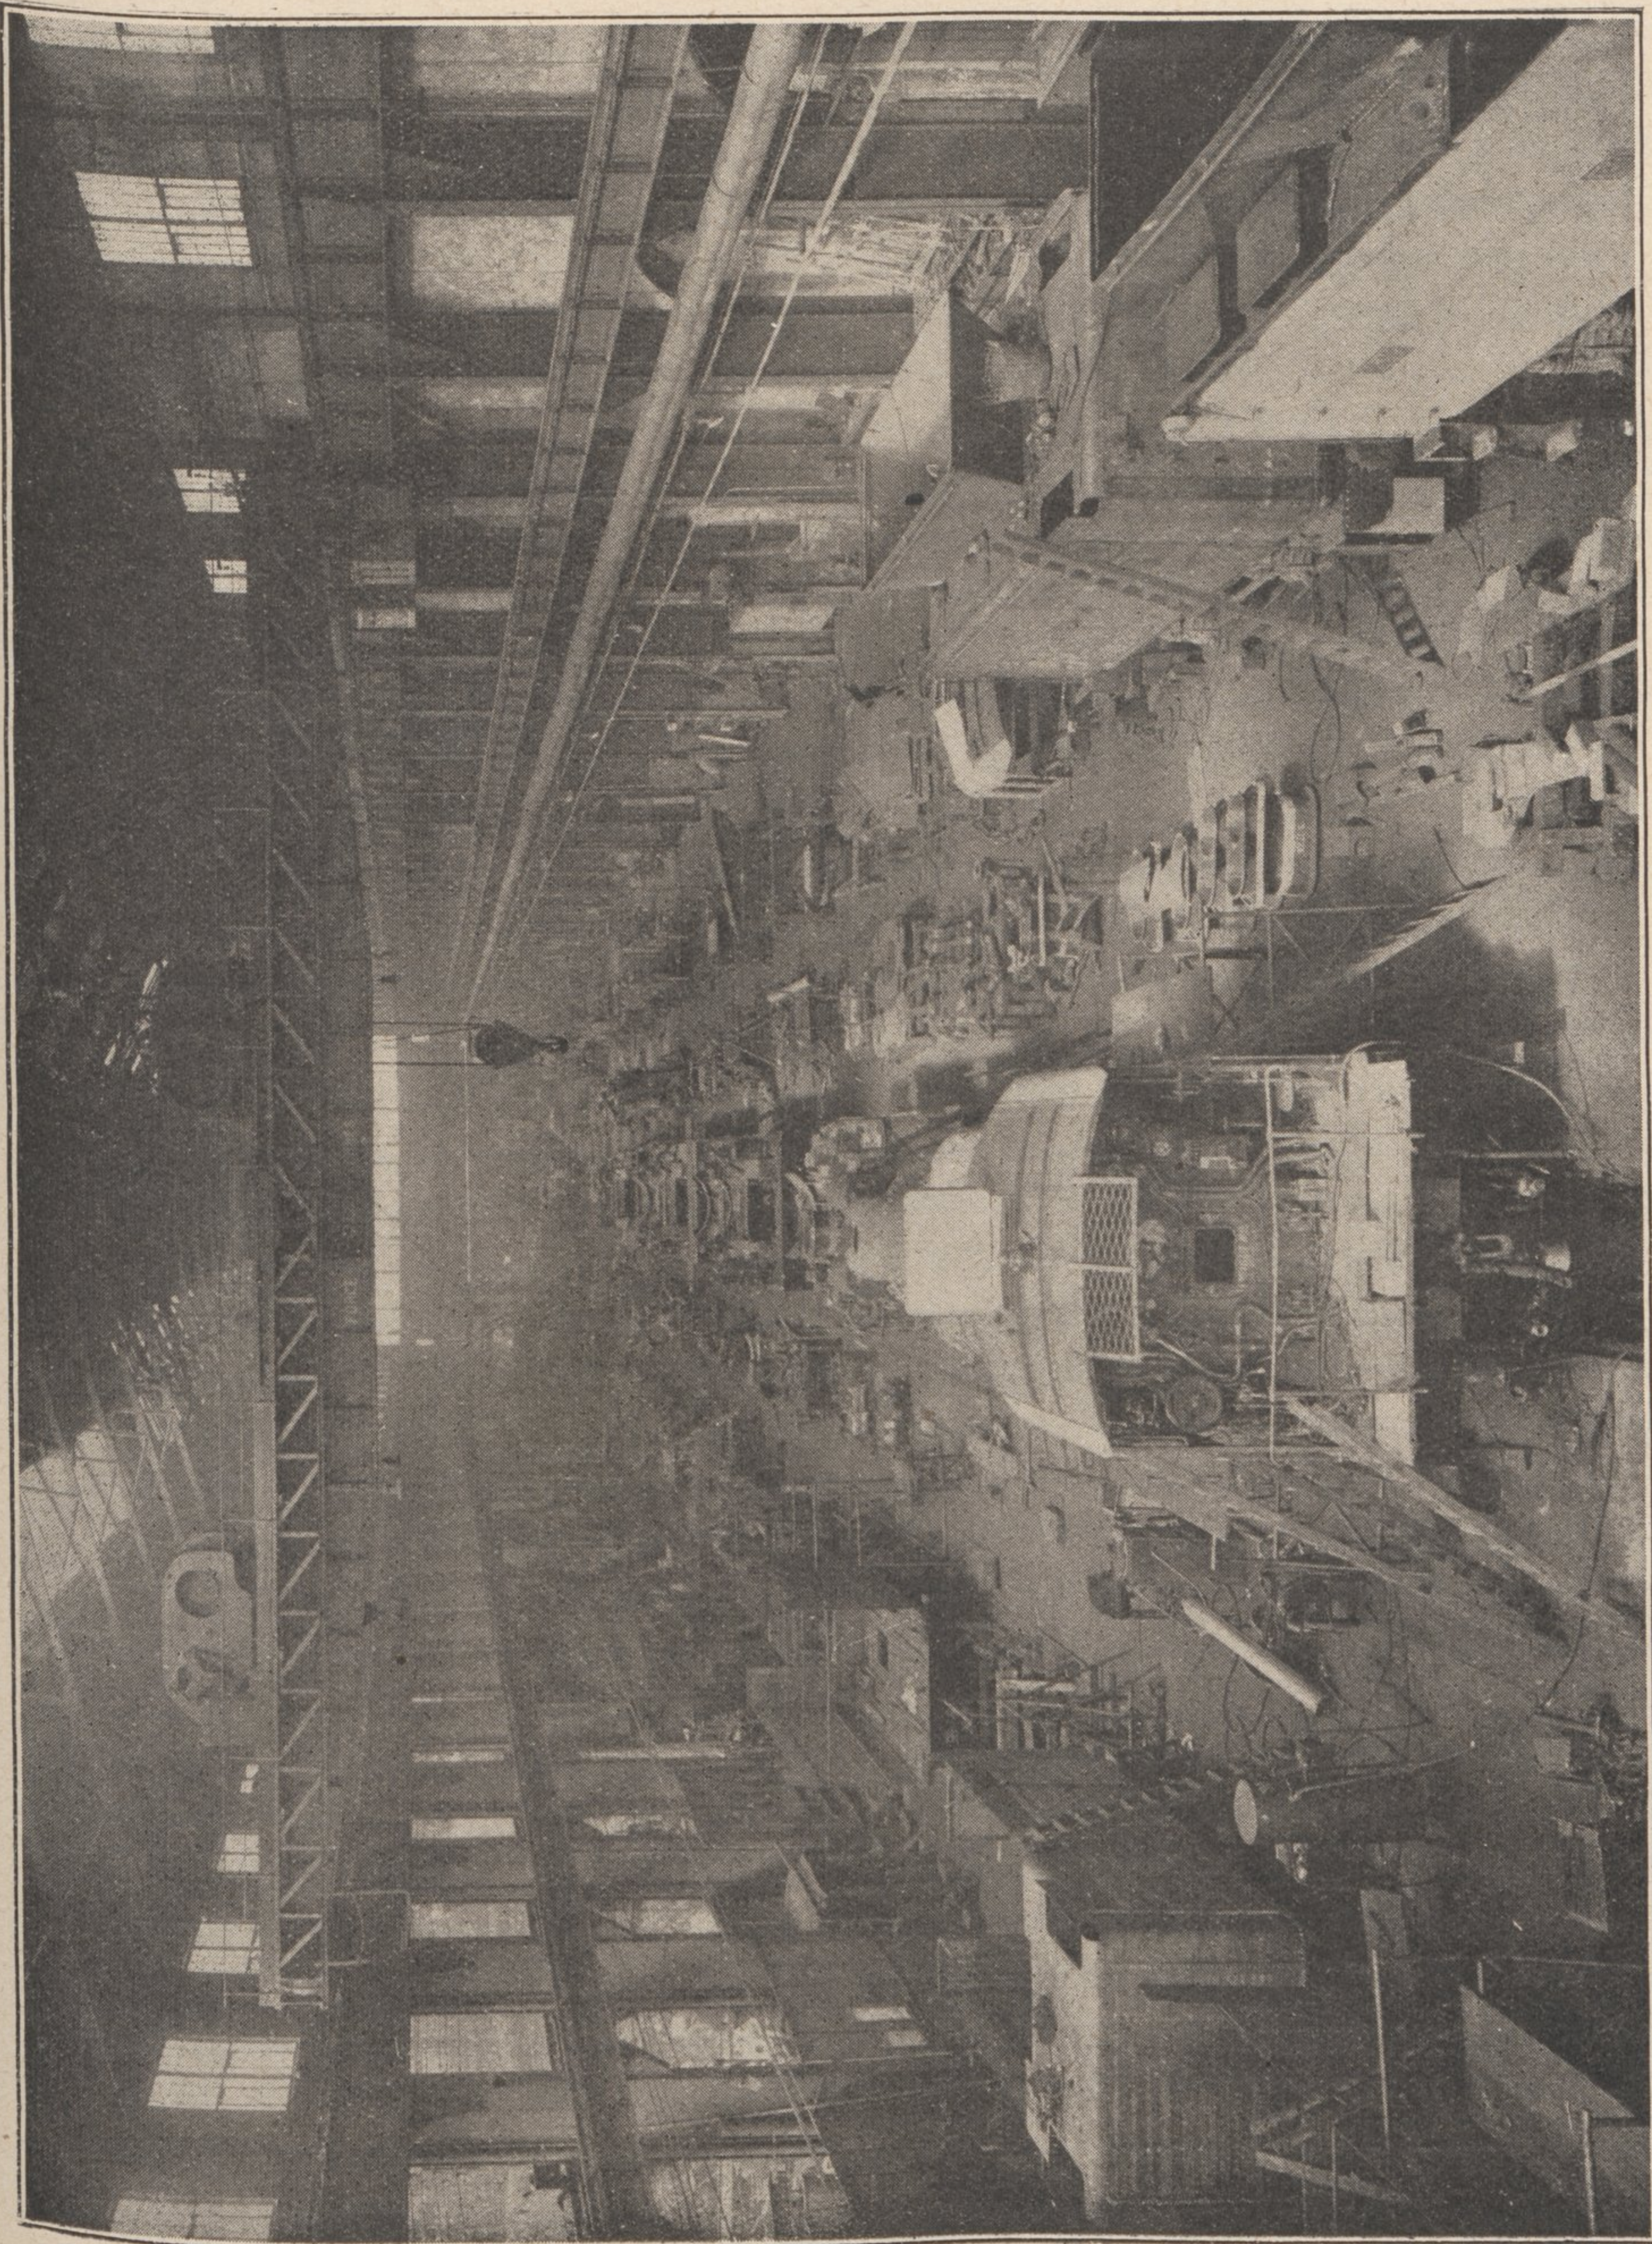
VUE D'ENSEMBLE DE LA CHAÎNE DE MONTAGE DES LOCOMOTIVES 4700
